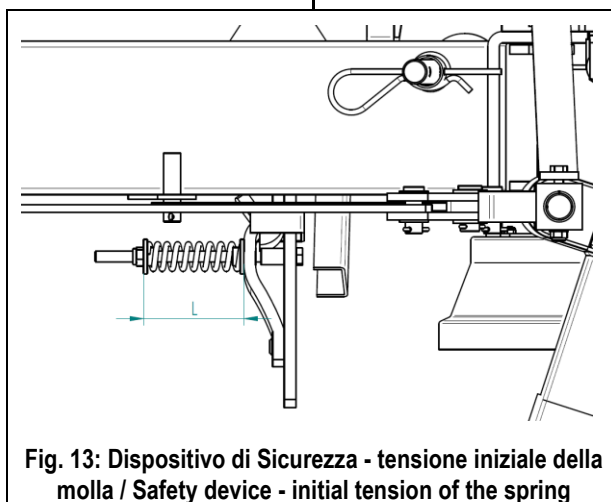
Dispositivo di Sicurezza - tensione iniziale della molla / Safety device - initial tension of the spring
